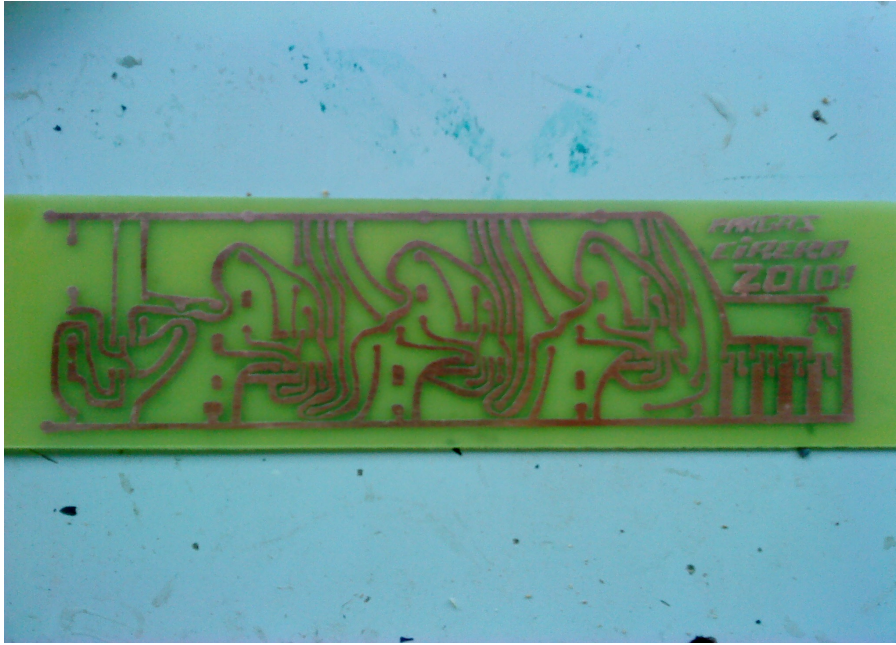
Acabat final de la placa, llesta per fer els forats i soldar-hi els components.
